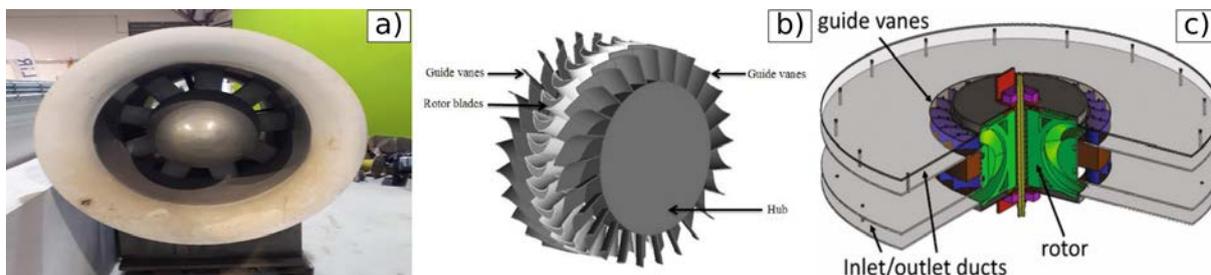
a) Turbina Wells. b) Turbina de impulso [4]. c) Turbina biradial [5].
